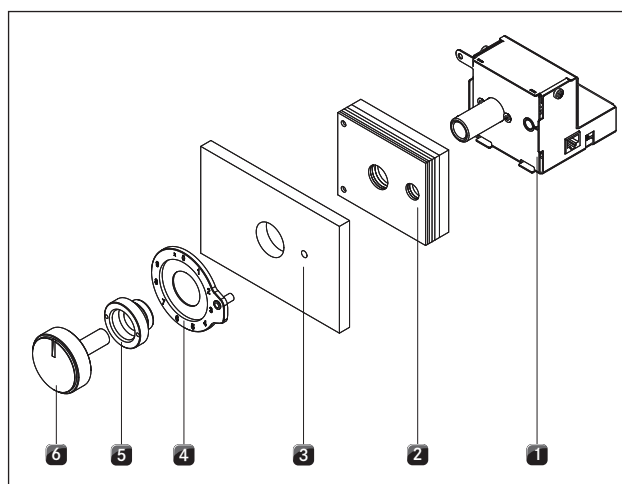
Montážne rozmery univerzálnej radiacej jednotky
